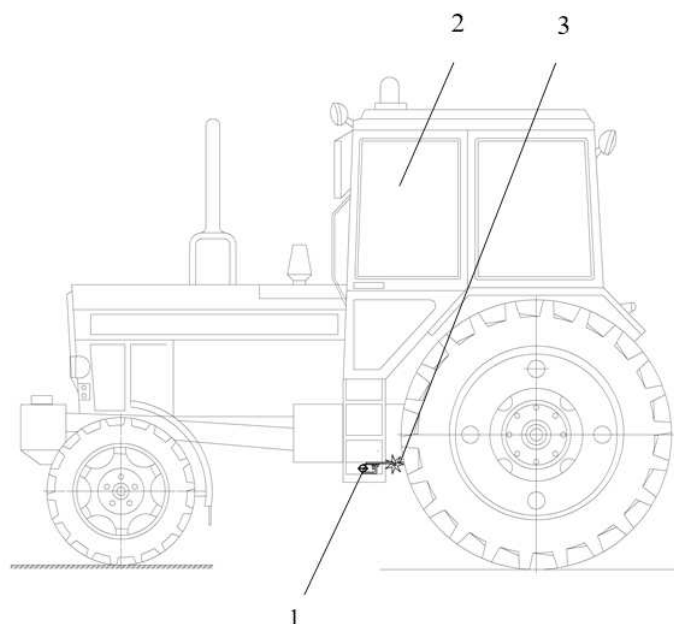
Общий вид трактора с установленным устройством (комбинированный очиститель протектора колёсного движителя): 1 – устройство; 2 – трактор; 3 – полимерно-композитные очистители с лучеобразными вычищающими элементами
